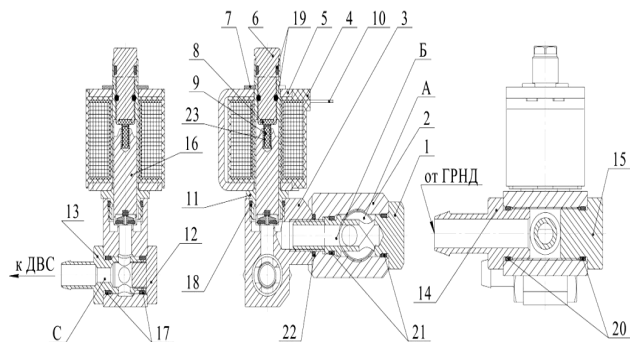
Конструкция опытного образца ЭДГ для двигателя 6ГЧН 13/14: 1 – винт крепежный; 2 – рампа соединительная; 3 – корпус дозатора; 4 – катушка электромагнита; 5 – скоба электромагнита; 6 – винт регулировочный; 7 – шайба стопорная; 8 – вставка демпферная; 9 – стержень направляющий; 10 – контактные клеммы; 11 – корпус клапана дозатора; 12 – пробка расходного жиклера; 13 – жиклер расходный; 14 – штуцер подачи газа; 15 – пробка задняя; 16 – клапан-сердечник дозатора; 17–22 – резиновые уплотнительные кольца; 23 – пружина возвратная
